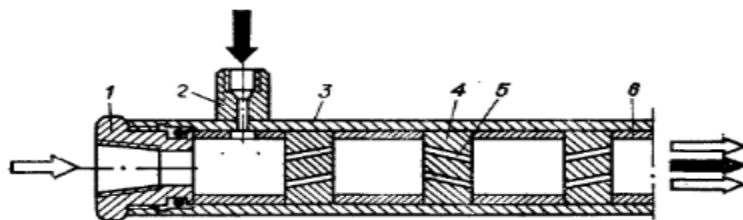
Статический смеситель с дисковыми вставками: 1, 2 – штуцеры для компонентов; 3 – корпус; 4 – диск; 5 – сквозной канал; 6 – втулка
